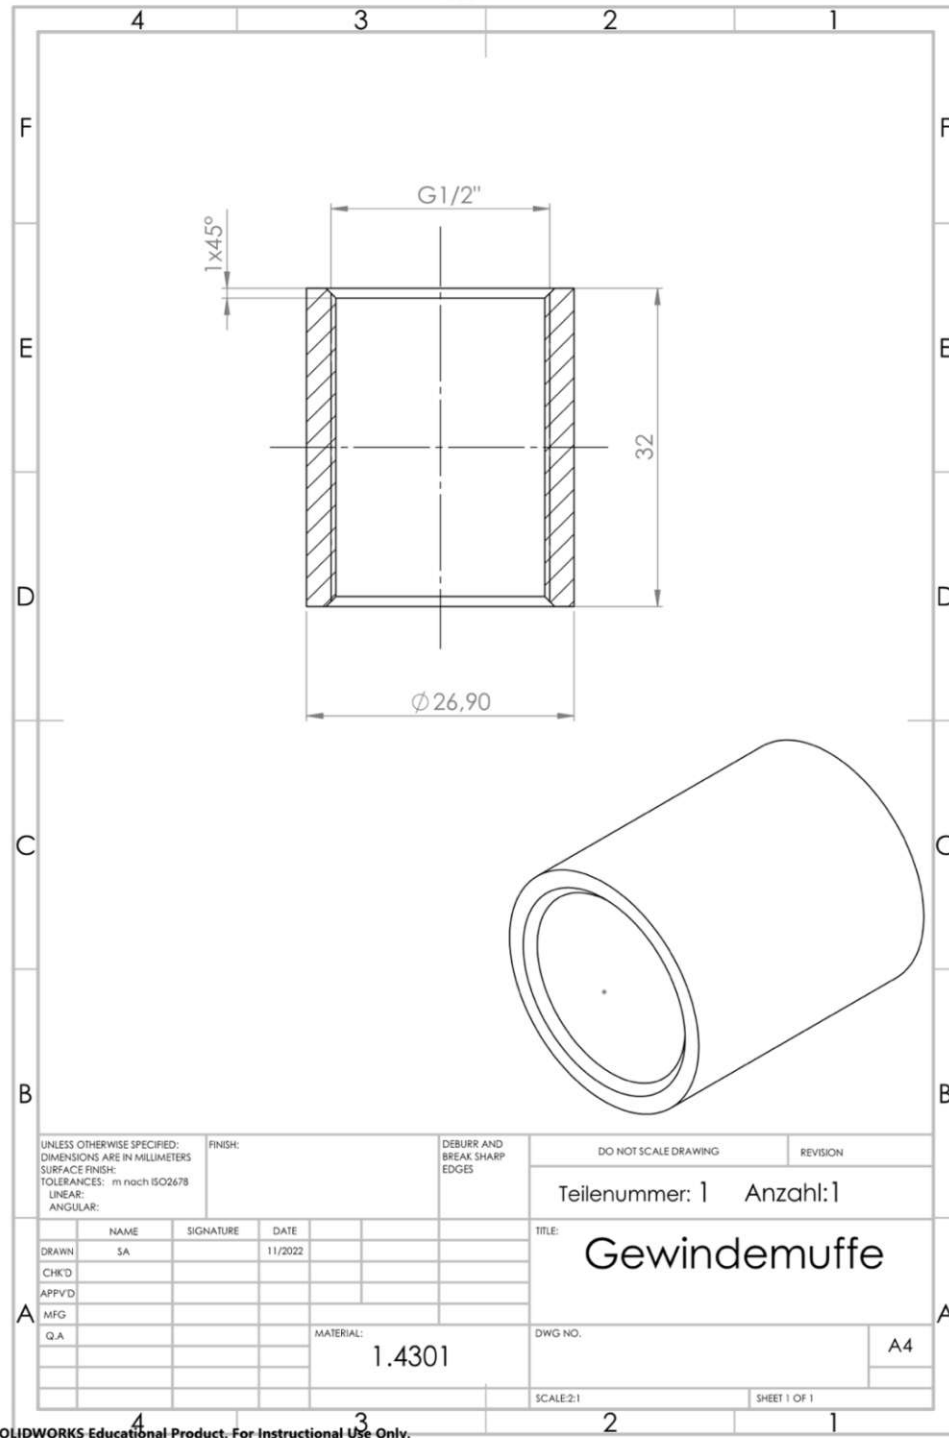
Technische Zeichnung der Gewindemuffe (Teilenummer 1)
